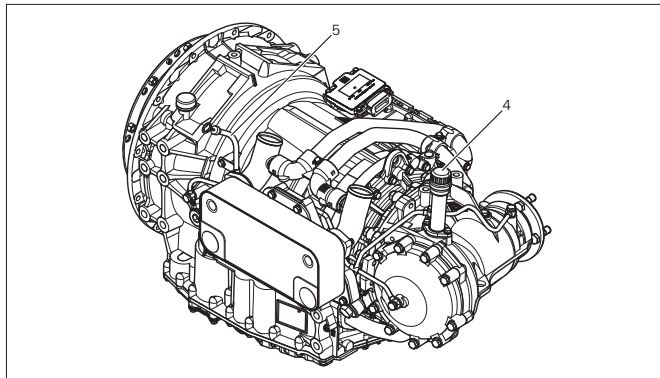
Коробка передач с угловым редуктором 80° RHD
